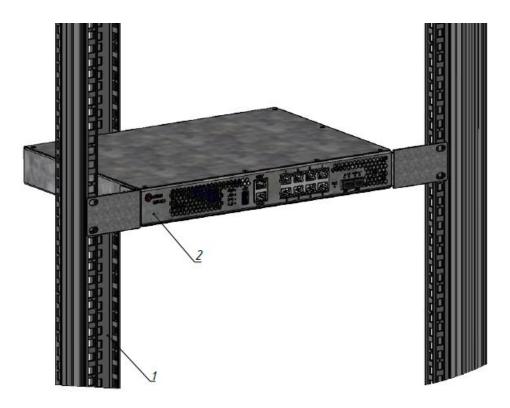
Установка маршрутизатора QSR-2200-10TBX-AC в стандартный шкаф
